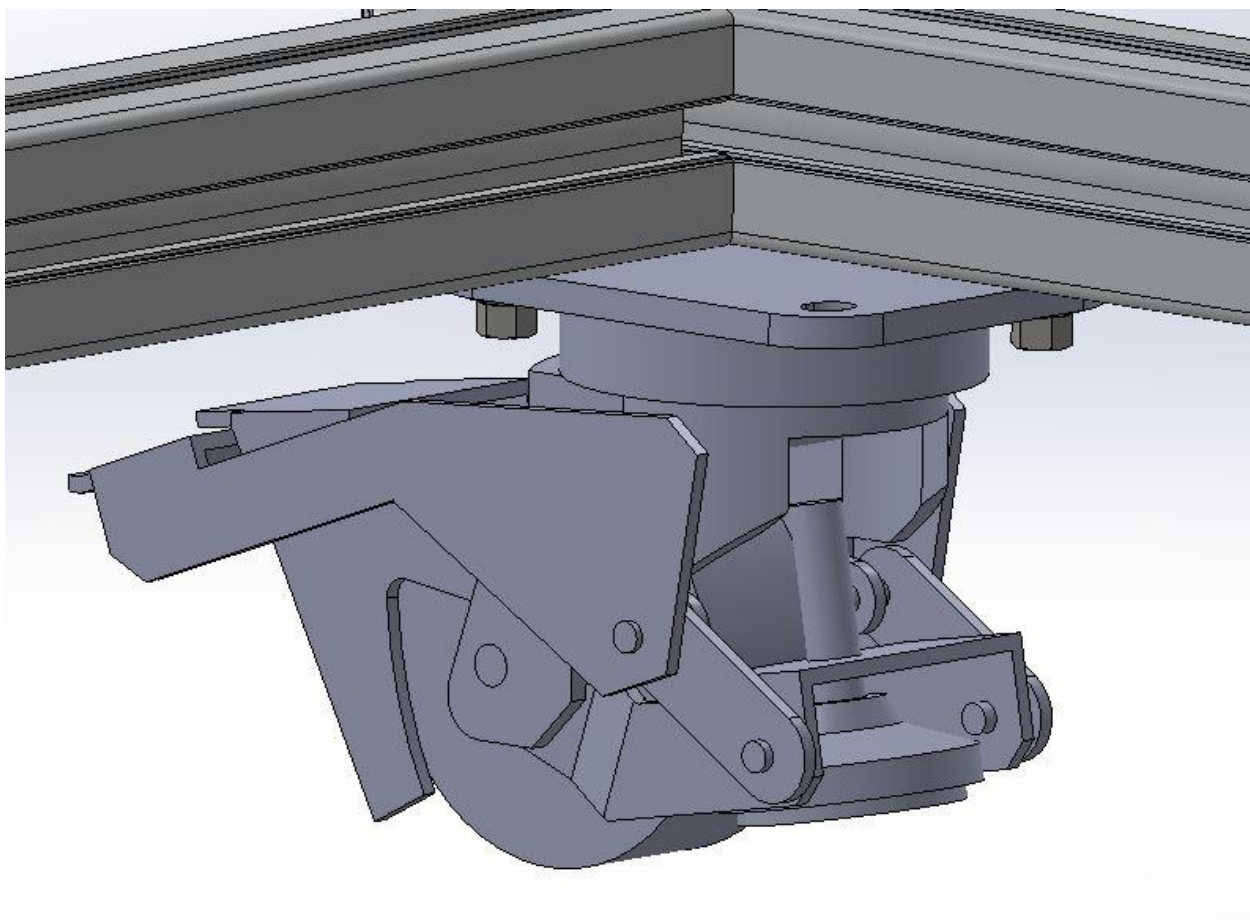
Izometrický pohled na rám tvořící prostor motoru
